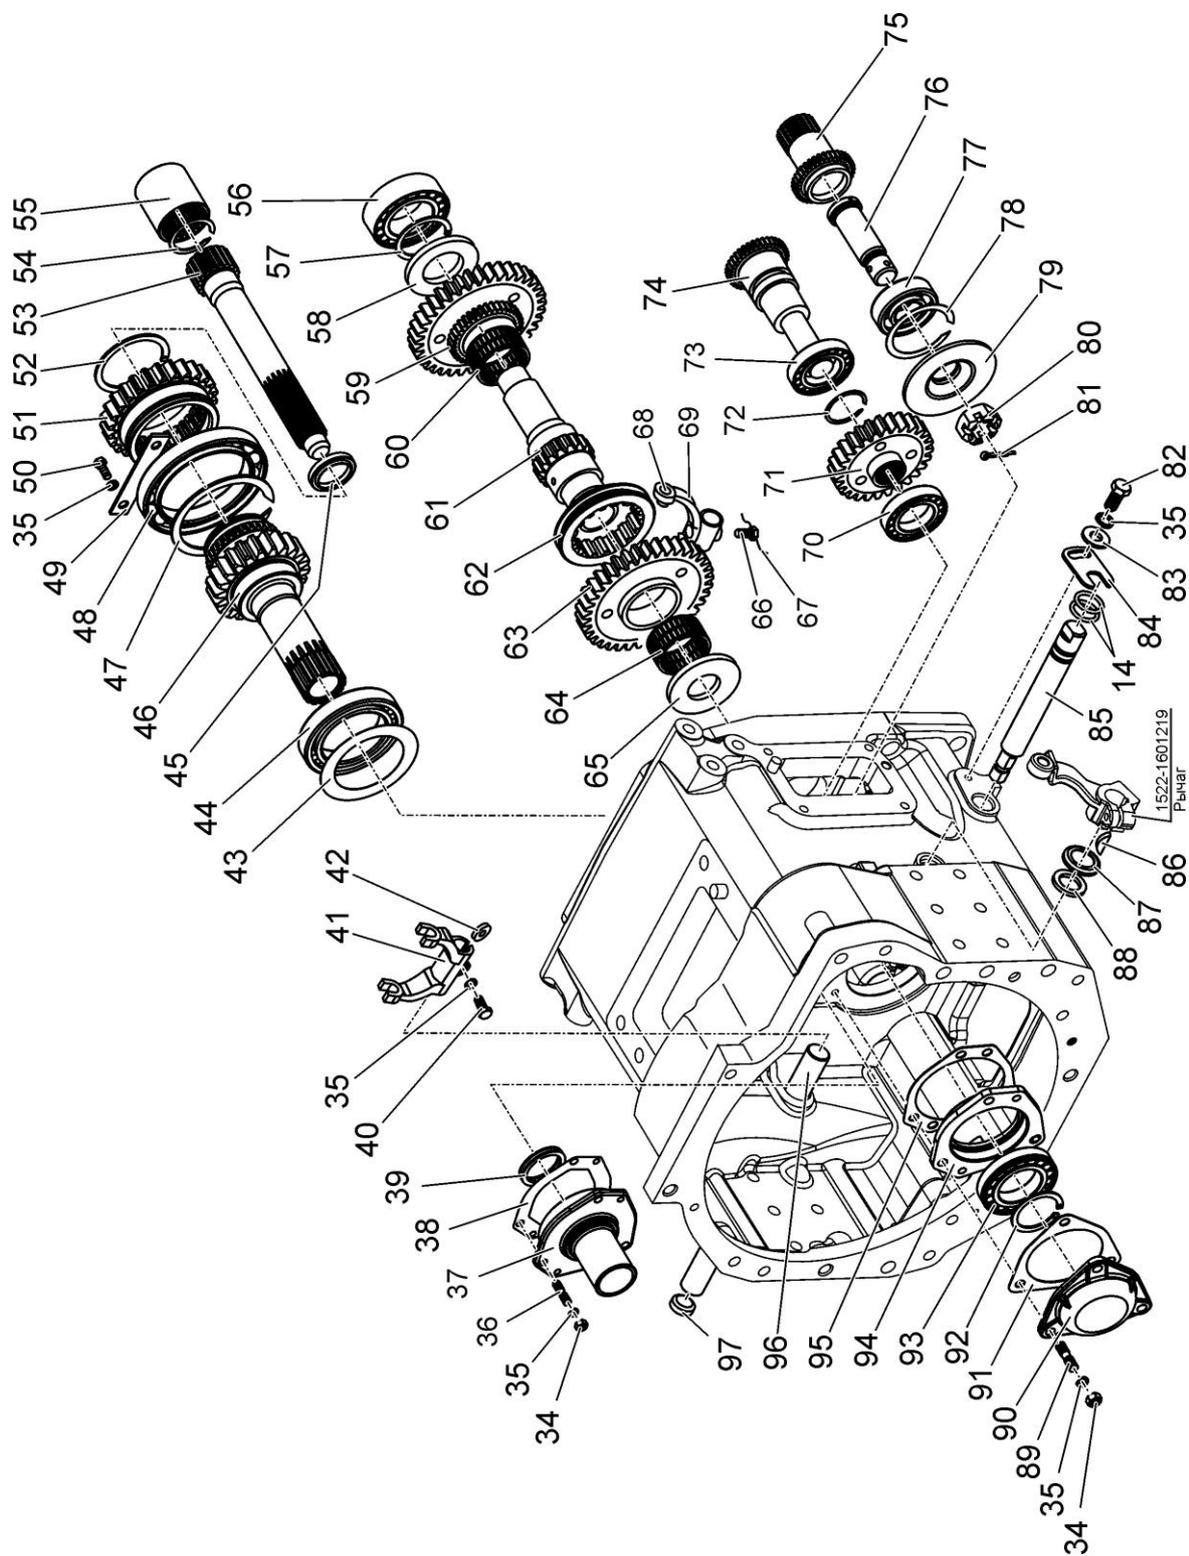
(лист 2 из 2) – Корпус сцепления. Горловина заливная. Шестерня. Кронштейн отводки. Вал. Втулка. Вилка. Вал-шестерня. Стакан
